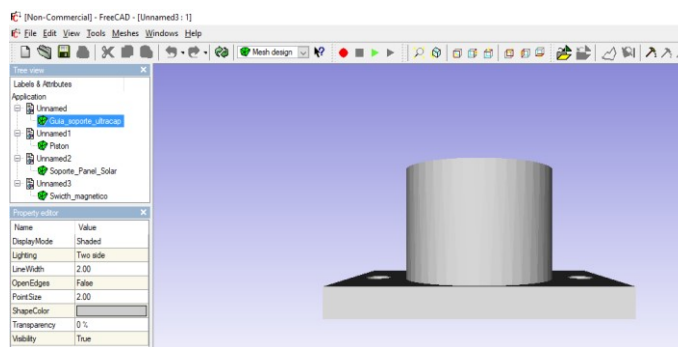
Diseño en FreeCAD del soporte de interruptor magnético.
